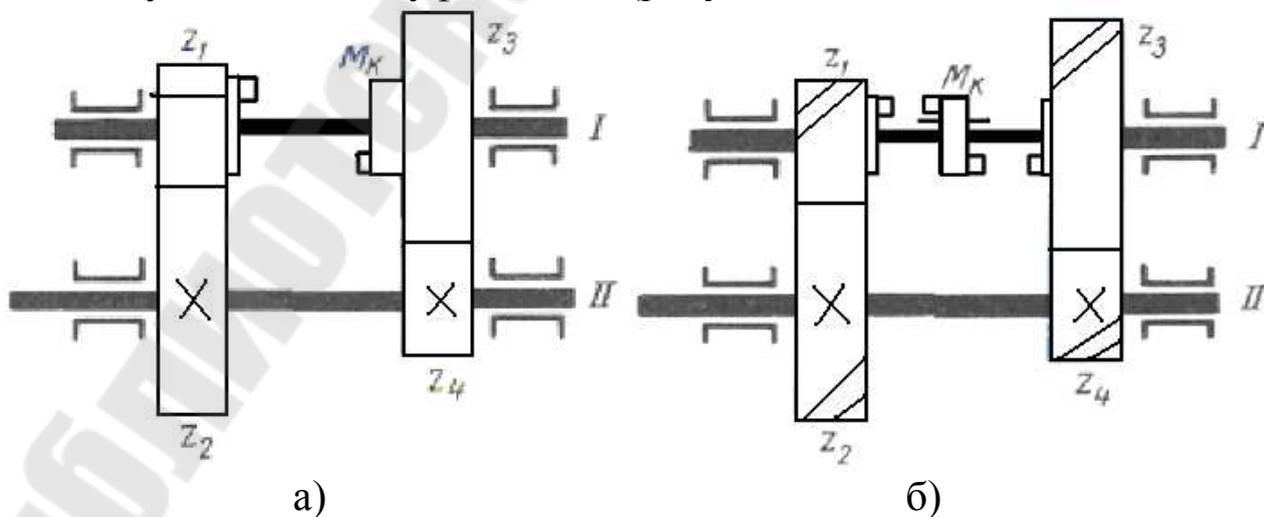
Схема шестерёнчатых коробок скоростей с кулачковыми муфтами: а – с односторонней муфтой; б – с двухсторонней муфтой
